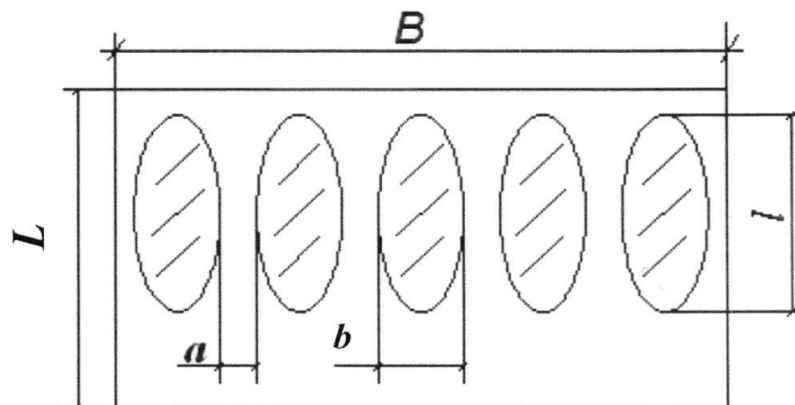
Расположение тестовых заготовок на люльке: В - ширина люльки; L - длина люльки; а - зазор между изделиями; в - ширина изделия; l - длина изделия
